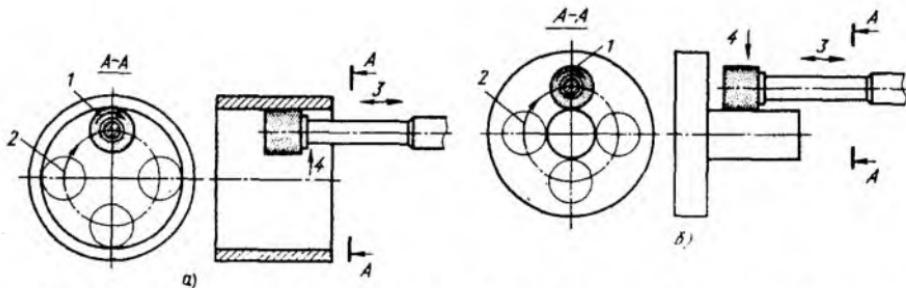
Внутреннее (а) и наружное (б) круглое шлифование при планетарном движении шпинделя и неподвижной заготовке
